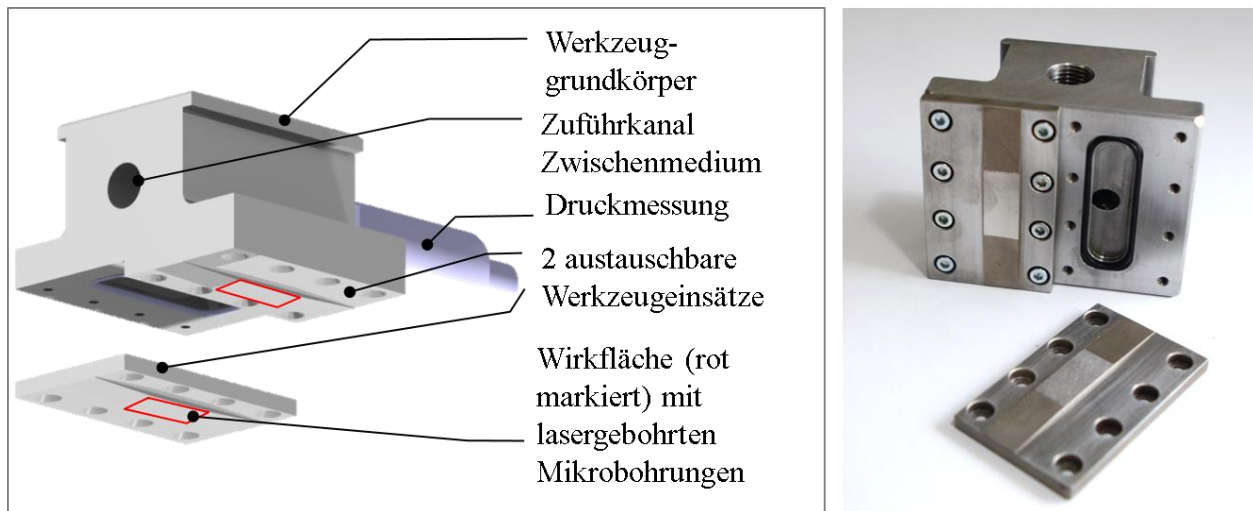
Werkzeug mit Zuleitungskanälen für das Wirkmedium und austauschbaren Werkzeugeinsätze mit lasergebohrten Mikrobohrungen für die aerostatische Schmierung im Streifenziehversuch.
